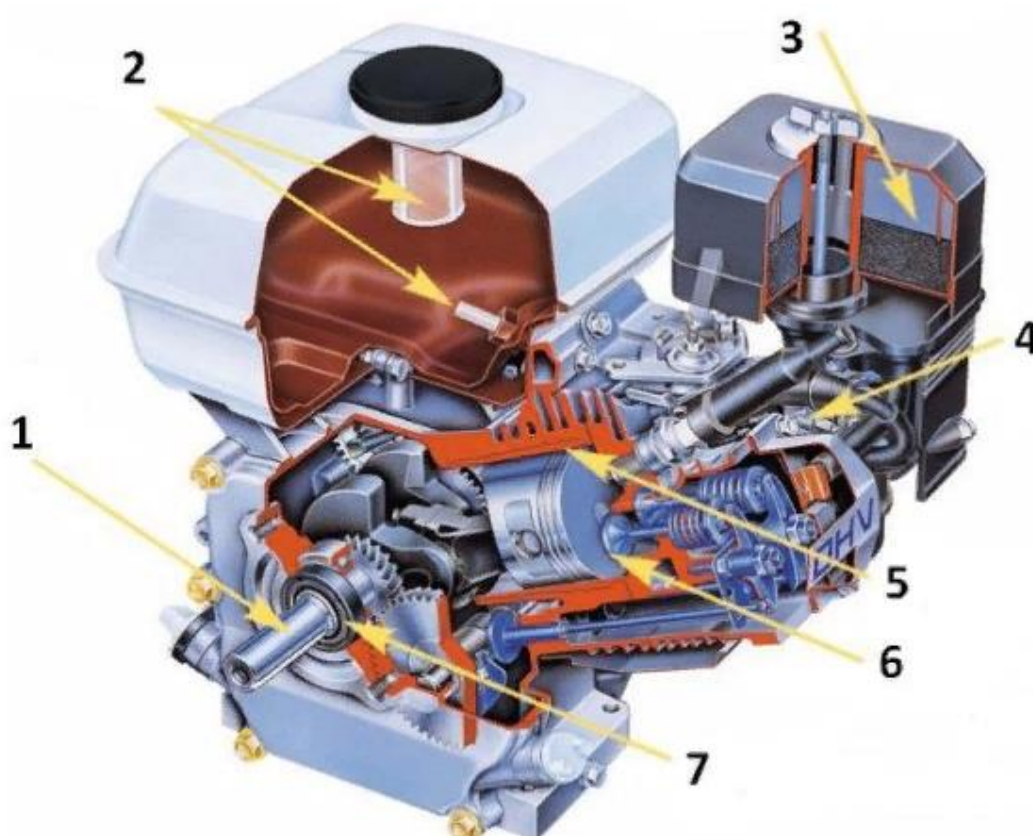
Устройство четырехтактного бензинового двигателя: 1 – кованый коленвал; 2 – топливные фильтры; воздушный фильтр; 4 – электронное зажигание; 5 – цилиндр; 6 – клапана; 7 – опорный подшипник
